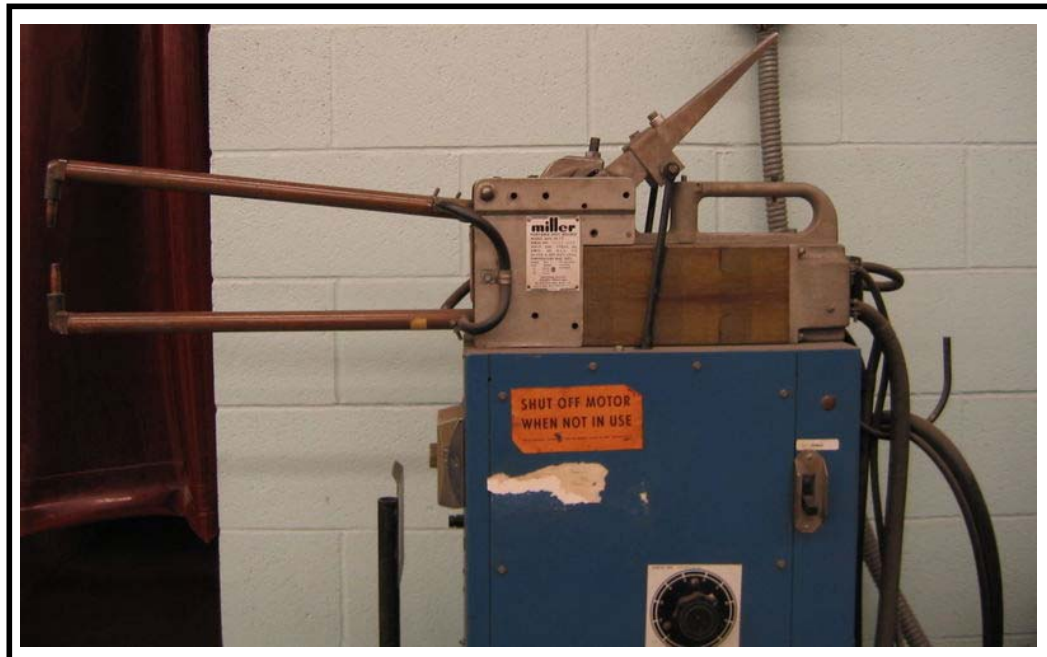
EQUIPO DE LA SOLADADURA DE PUNTO
